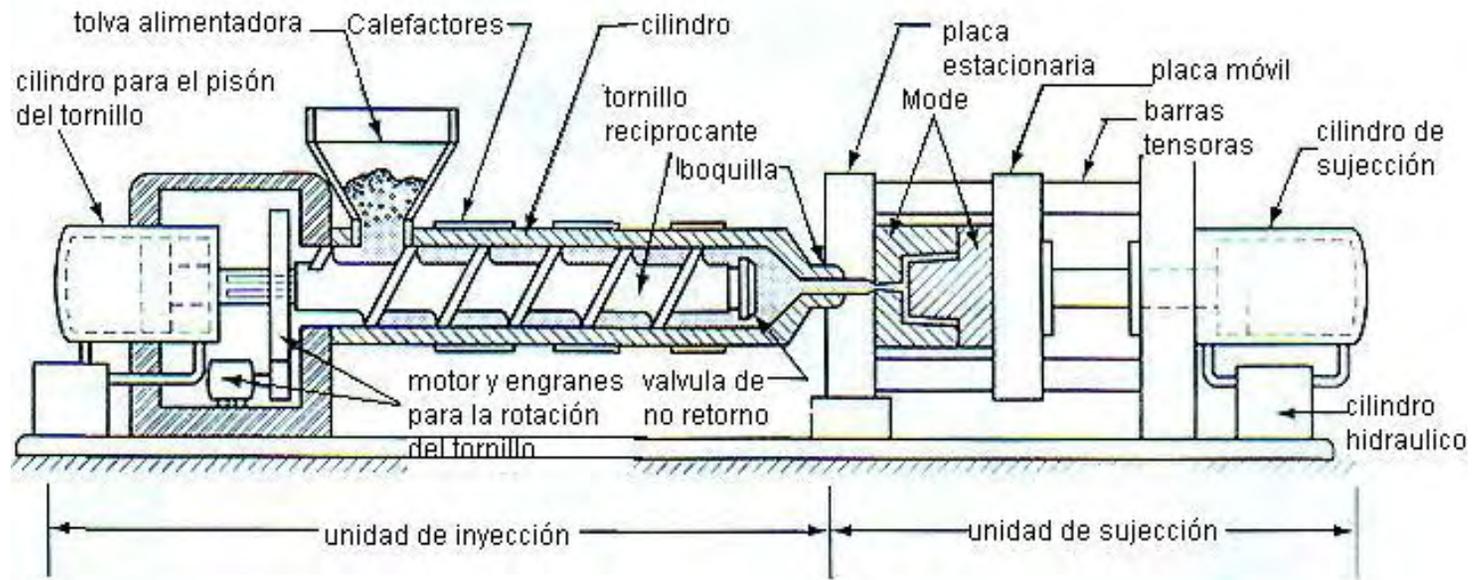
Diseño de máquina empleada durante la técnica de moldeo por inyección. (51)
